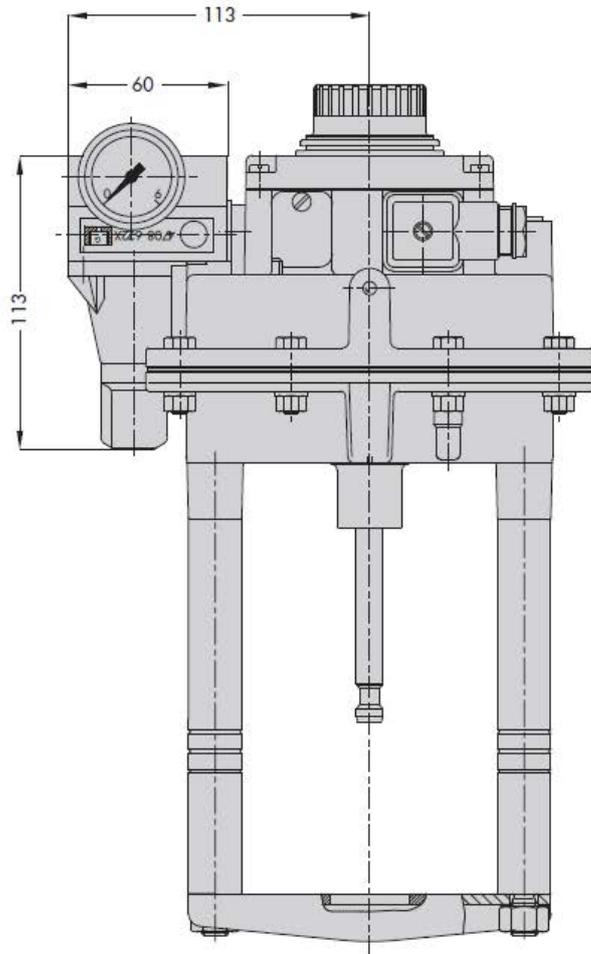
• Регулятор давления типов 4708-62 для пневматического привода тип 3372
